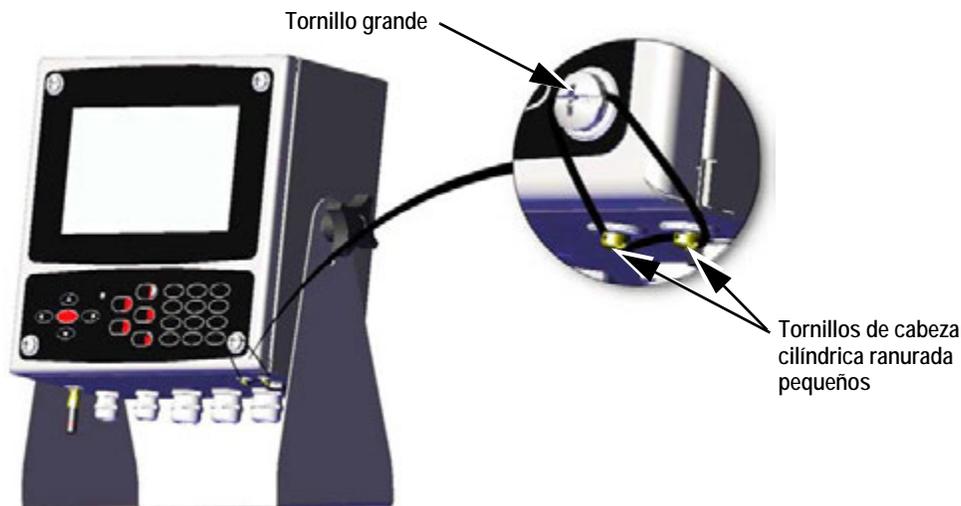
Sellado de la puerta frontal (Montaje universal)
